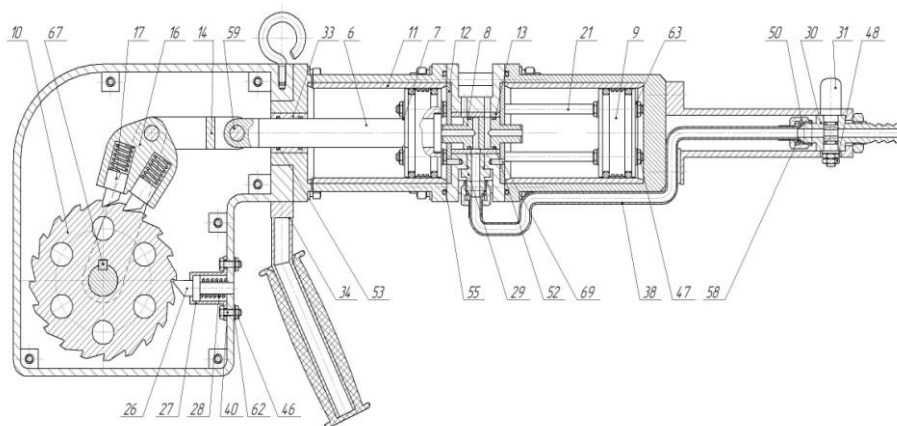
Схема пневматического гайковерта с кривошипом
